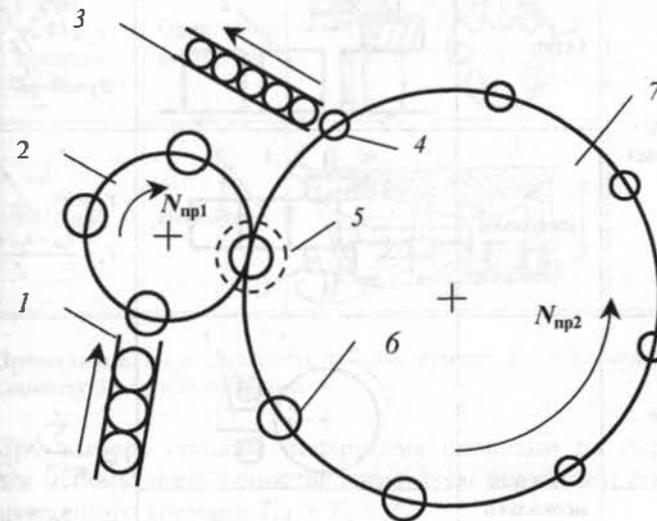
Движение детали при роторной непрерывной обработке:
